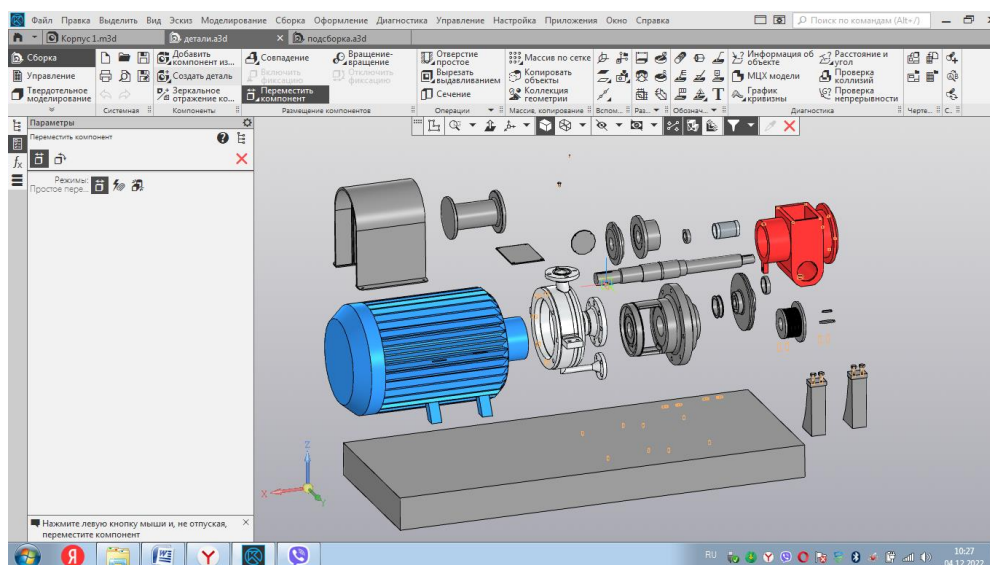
Детали и компоненты для сборки насосного агрегата
